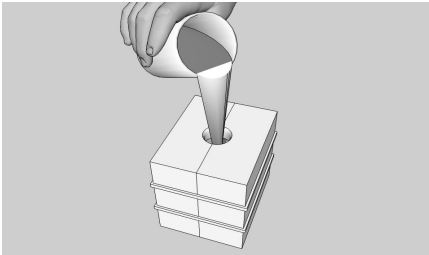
Vertendo material de moldagem para fazer novas peças.
